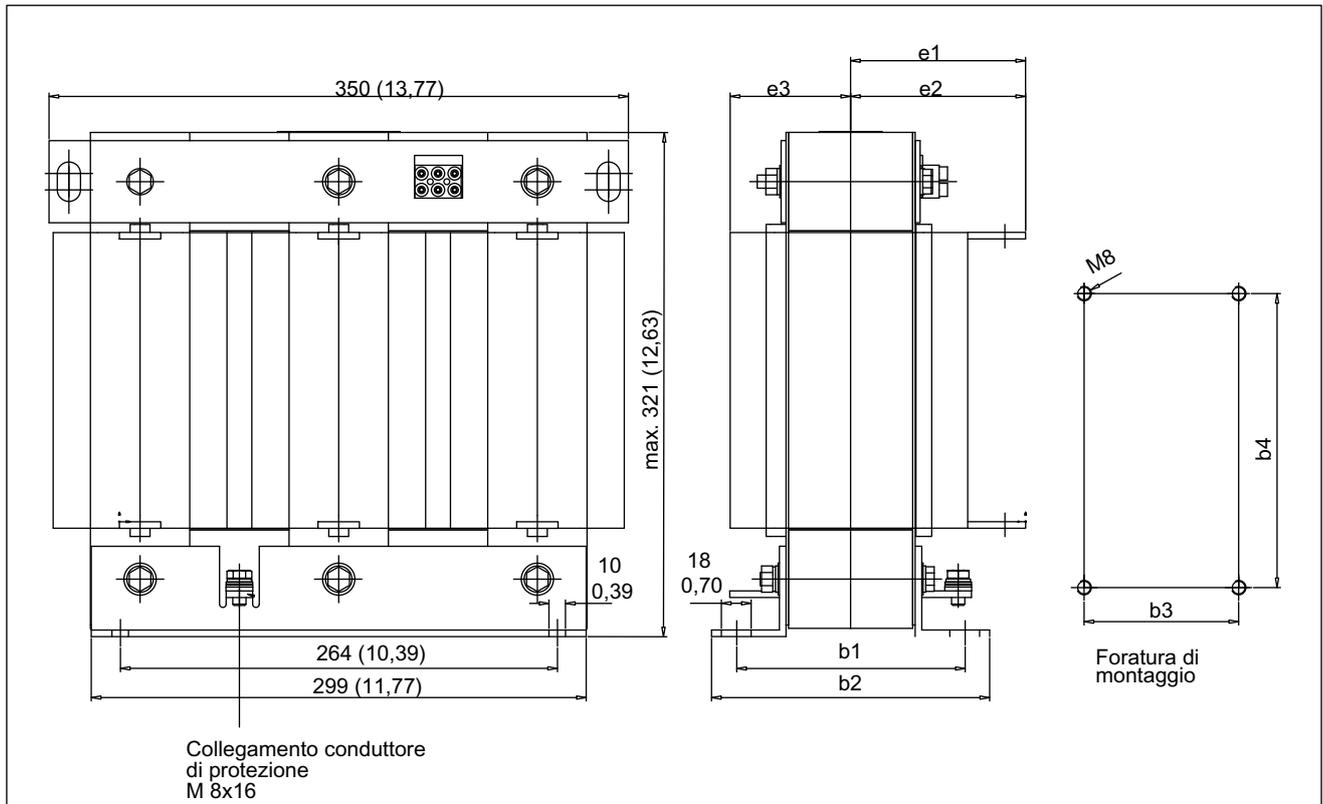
Disegno quotato: Bobina motore, grandezza costruttiva FSF
